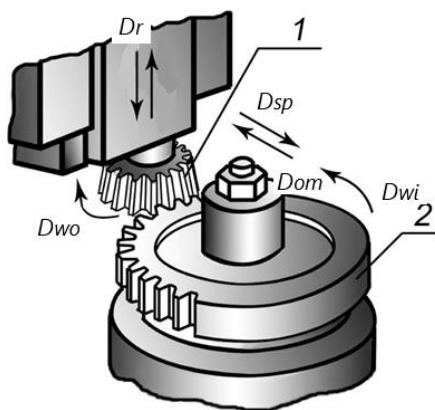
Схема нарезания зубьев цилиндрического прямозубого колеса зуборезным долбяком
